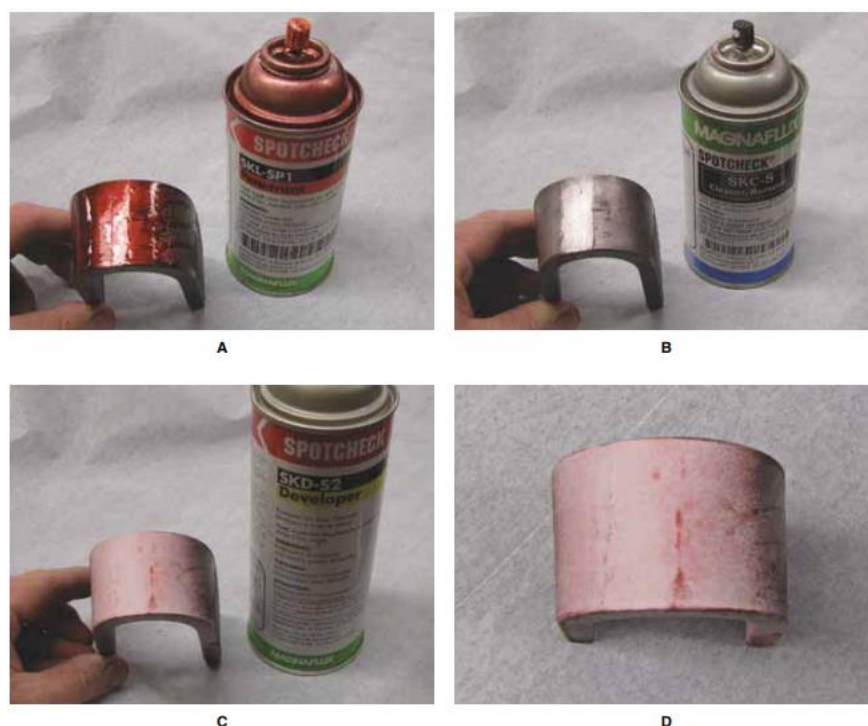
Secuencia de prueba de tinte penetrante. A-El líquido penetrante se aplica a la soldadura. B-El penetrante se limpia de la soldadura. C-El revelador se aplica a la soldadura. D-La soldadura se inspecciona para detectar discontinuidades que aparecieron después de que se aplicó el revelador
